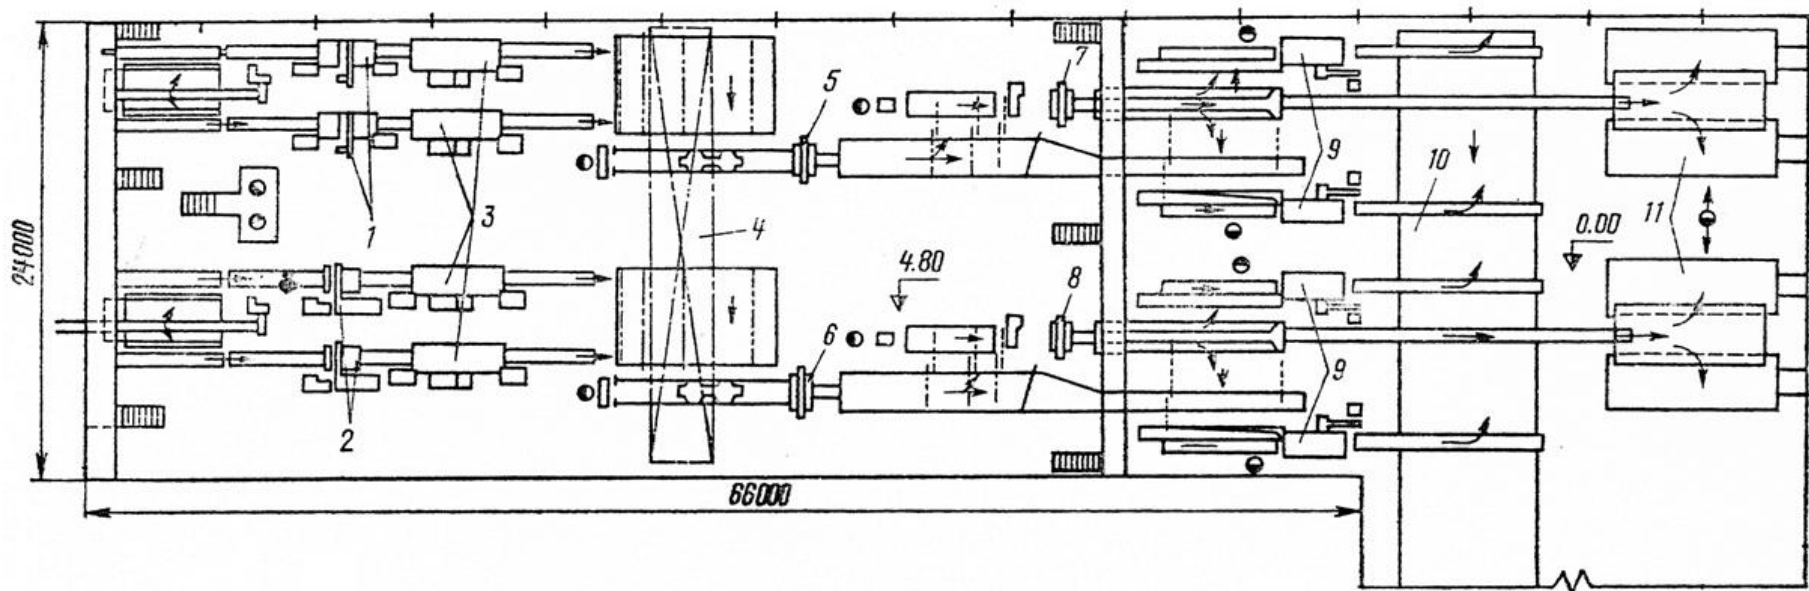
Схема двухпоточного лесопильного цеха (план 2-го этажа)
